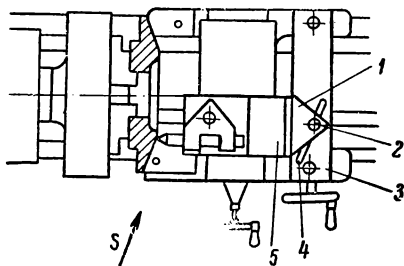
Схема обработки конической шестерни с помощью специального копирного приспособления.
